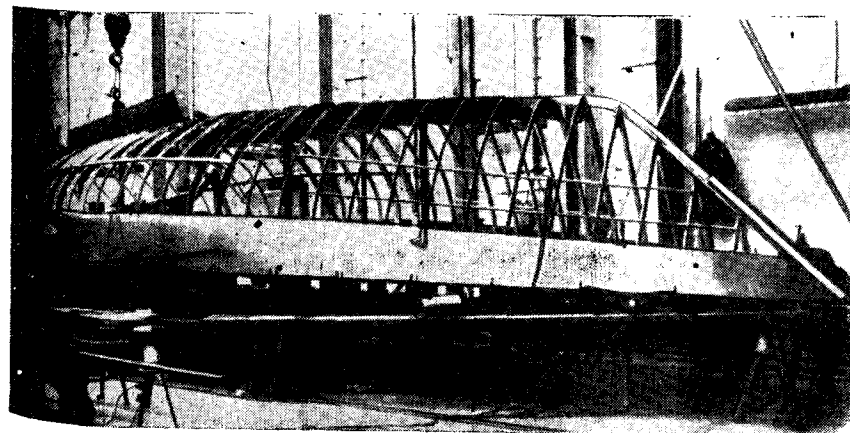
Сборка корпуса в положении килем вверх на палубе. Обшивать корпус начинают с ширстрека.
